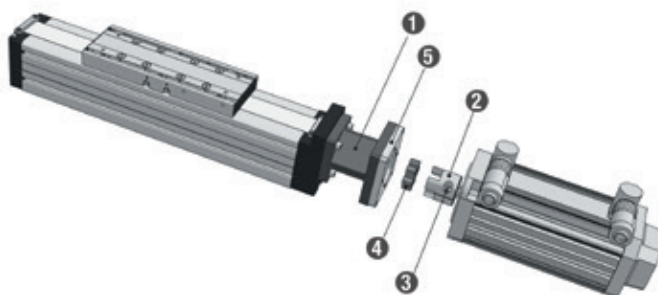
Motormontage an Linearachsen mit Spindelantrieb und Kupplungsglocke
